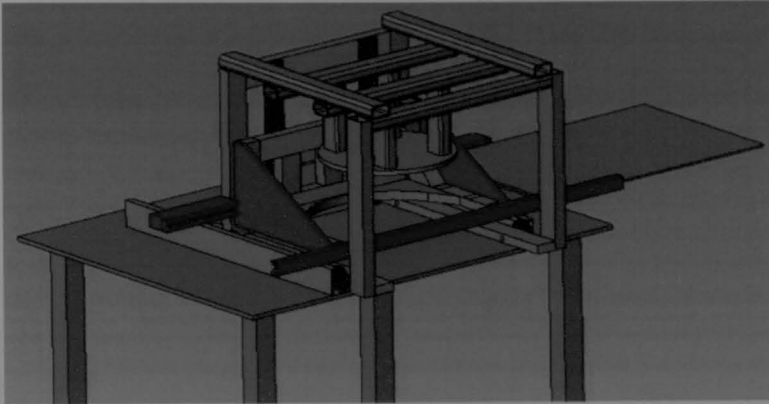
34 – Projecto CAD 3D de uma máquina de desmoldar.
